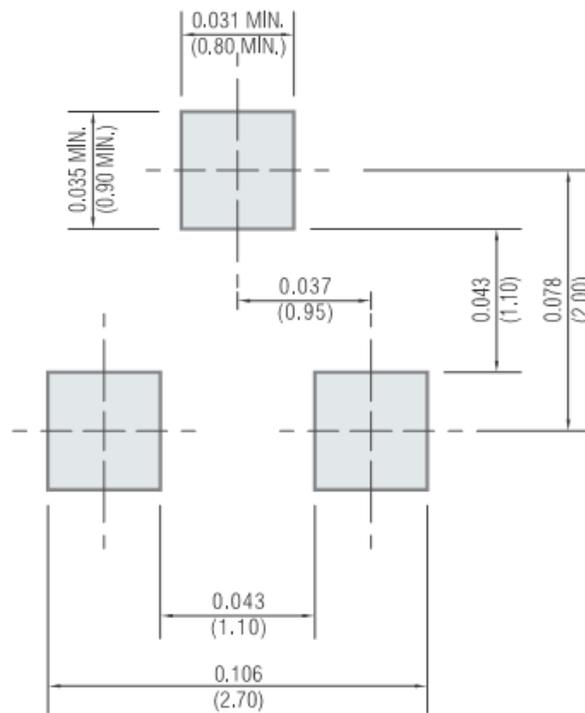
Рекомендованные производителем размеры контактных площадок для корпуса типа SOT-23
